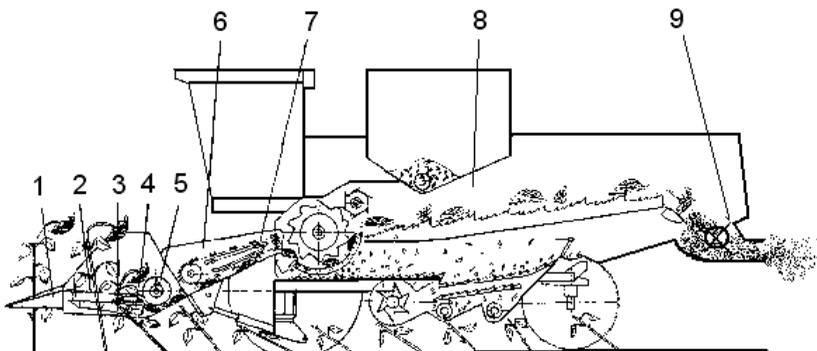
Технологическая схема приспособления в агрегате с зерноуборочным комбайном: 1 - мус; 2 - цепной транспортер; 3 - режущий аппарат; 4 - приводная коробка русла; 5 - шнек; 6 - наклонная камера комбайна; 7 - транспортер наклонной камеры; 8 – молотилка комбайна; 9 - измельчитель корзинок
